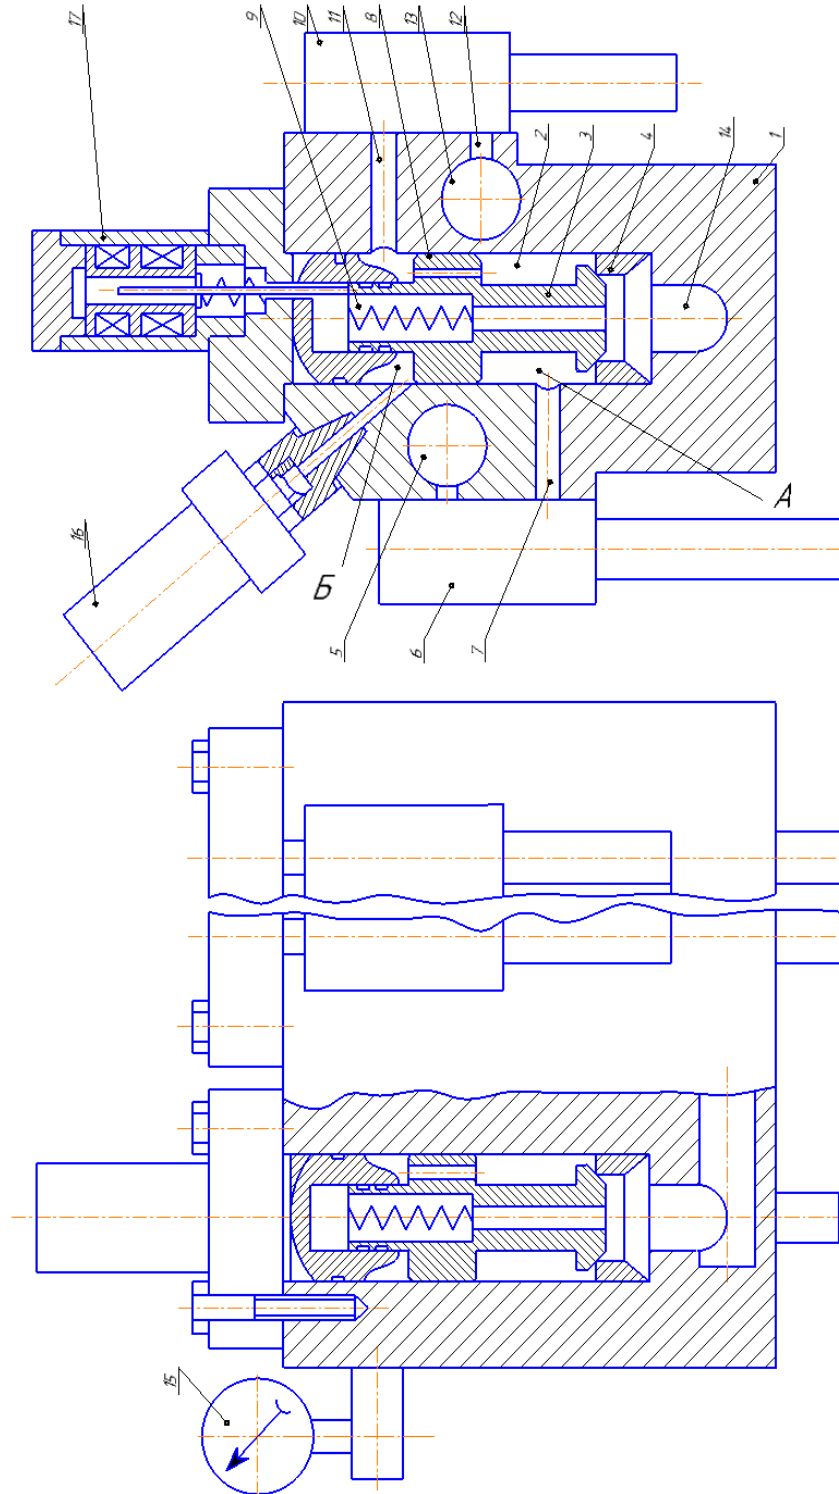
Установка для випробовування клапанів: 1 – корпус; 2 – отвори під клапани; 3 – перепускний клапан; 4 – гніздо; 5 – магістральний канал; 6 – пристрій подачі мастила; 7, 11, 12 – канали; 8 – дроселюючий отвір; 9 – пружина; 10 – пілот; 13 – зливна магістраль; 14 – зливний канал; 15 – манометр; 16 – датчик переміщення
